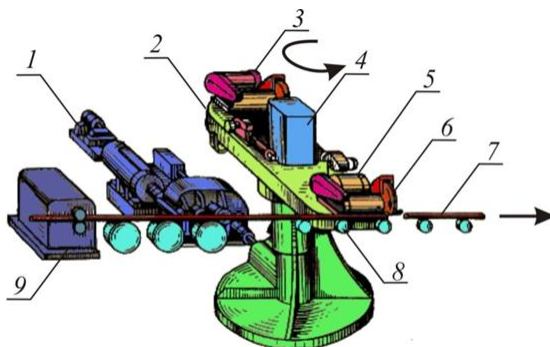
Летучая пила для резки труб: 1 – главный привод вращения стола; 2 – стол; 3, 5 – каретки; 4 – режущий механизм; 6 – режущий диск; 7 – труба; 8 – механизм подъема трубы; 9 – устройство синхронизации скоростей пилы и выхода трубы
